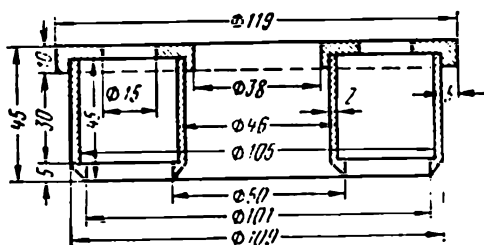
Разрез режущего приспособления для вырезки кольцевых образцов
